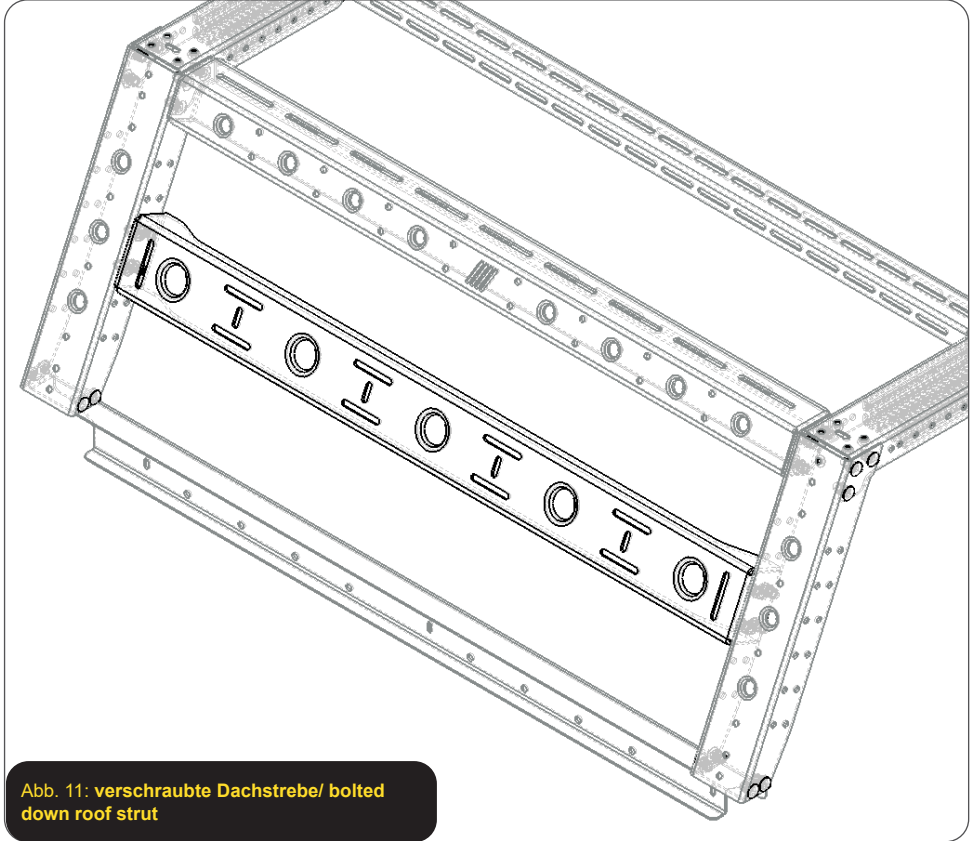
verschraubte Dachstrebe/ bolted down roof strut
